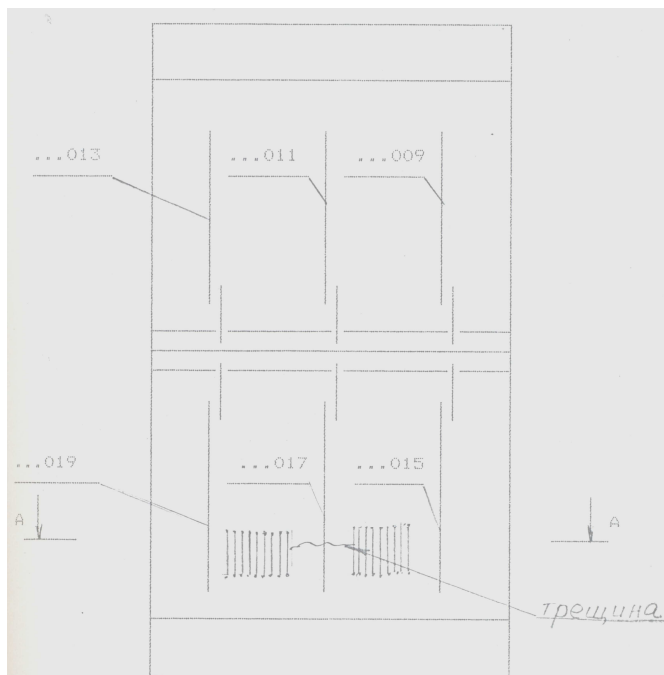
Схема расположения трещины и сигнализаторов разрушения на образце для испытаний
